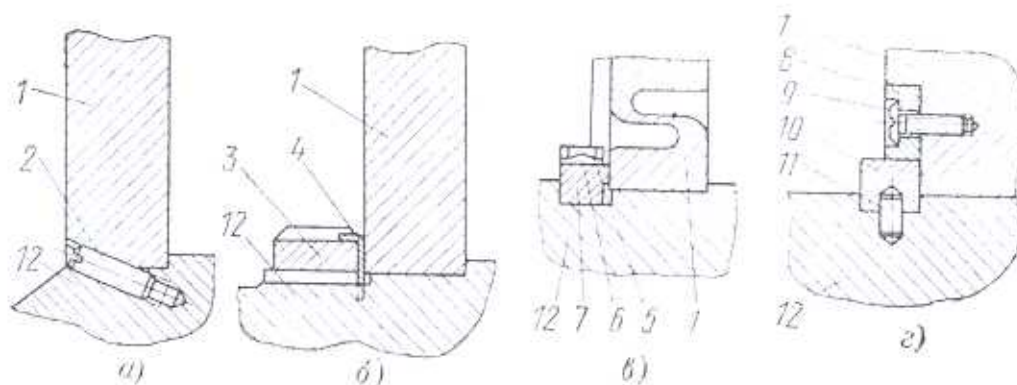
Крепление центрирующих колец стопорными винтами:
